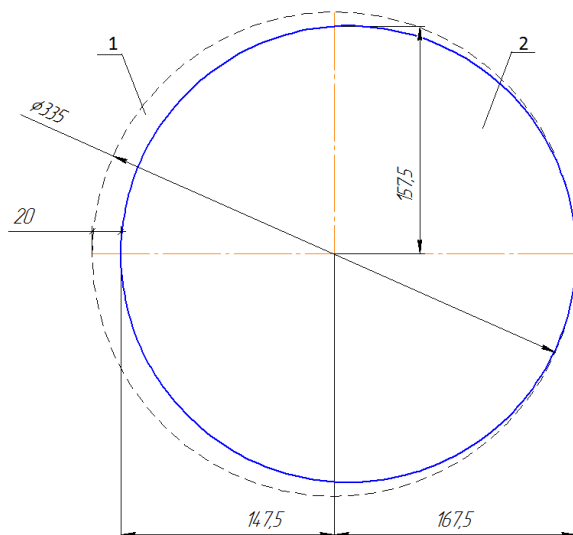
Расчетная и круглая заготовки (1-круглая заготовка, 2-расчетная заготовка)
